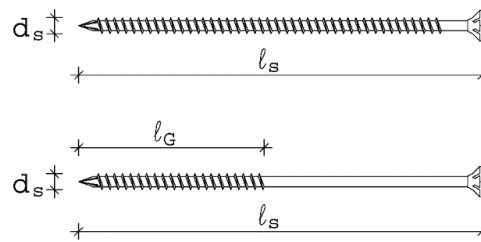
selbstbohrende Schrauben mit Voll- und Teilgewinde
